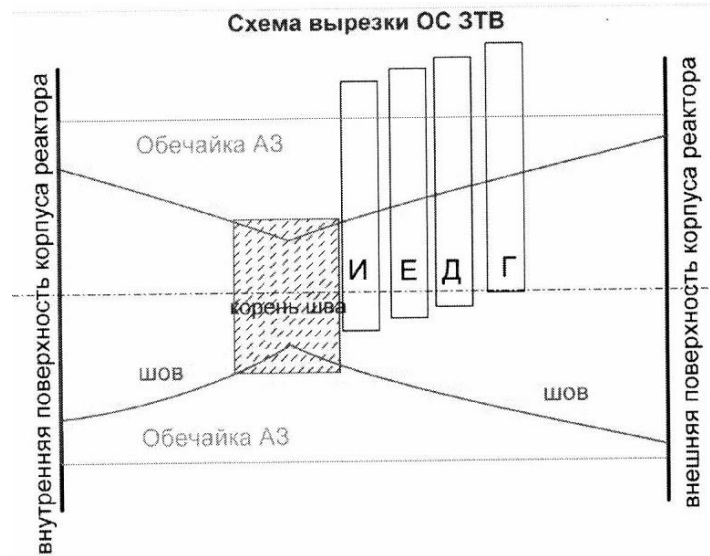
Схема вирізки зразків-свідків металу ЗТВ із зварної проби
